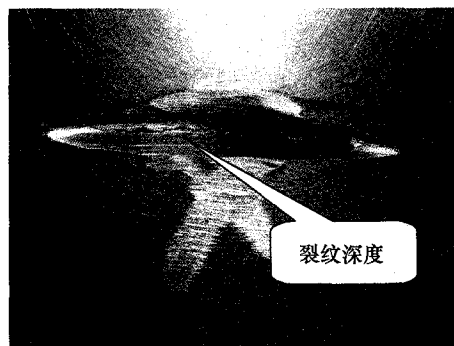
焊缝附近经打磨后的裂纹形貌
